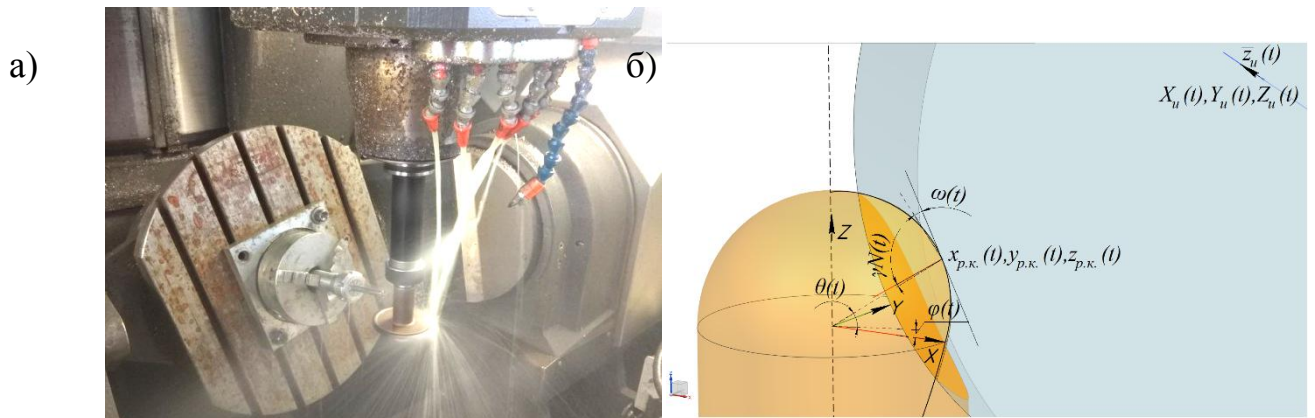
а) Заточка и б) моделирование процесса формообразования шлифовальным кругом концевой сферической фрезы на пятикоординатном фрезерном станке с ЧПУ Hedelius RS605 K20
